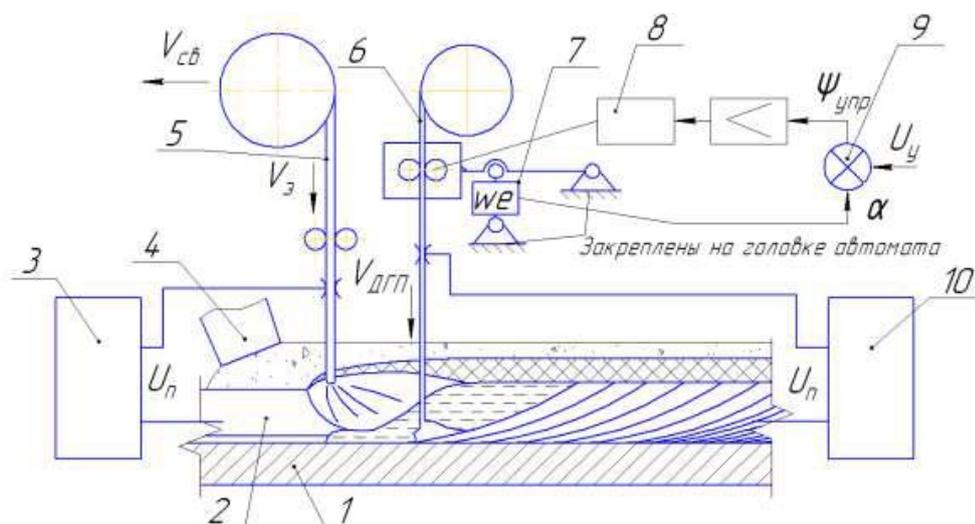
«Схема процесса сварки с ДГП под флюсом:
